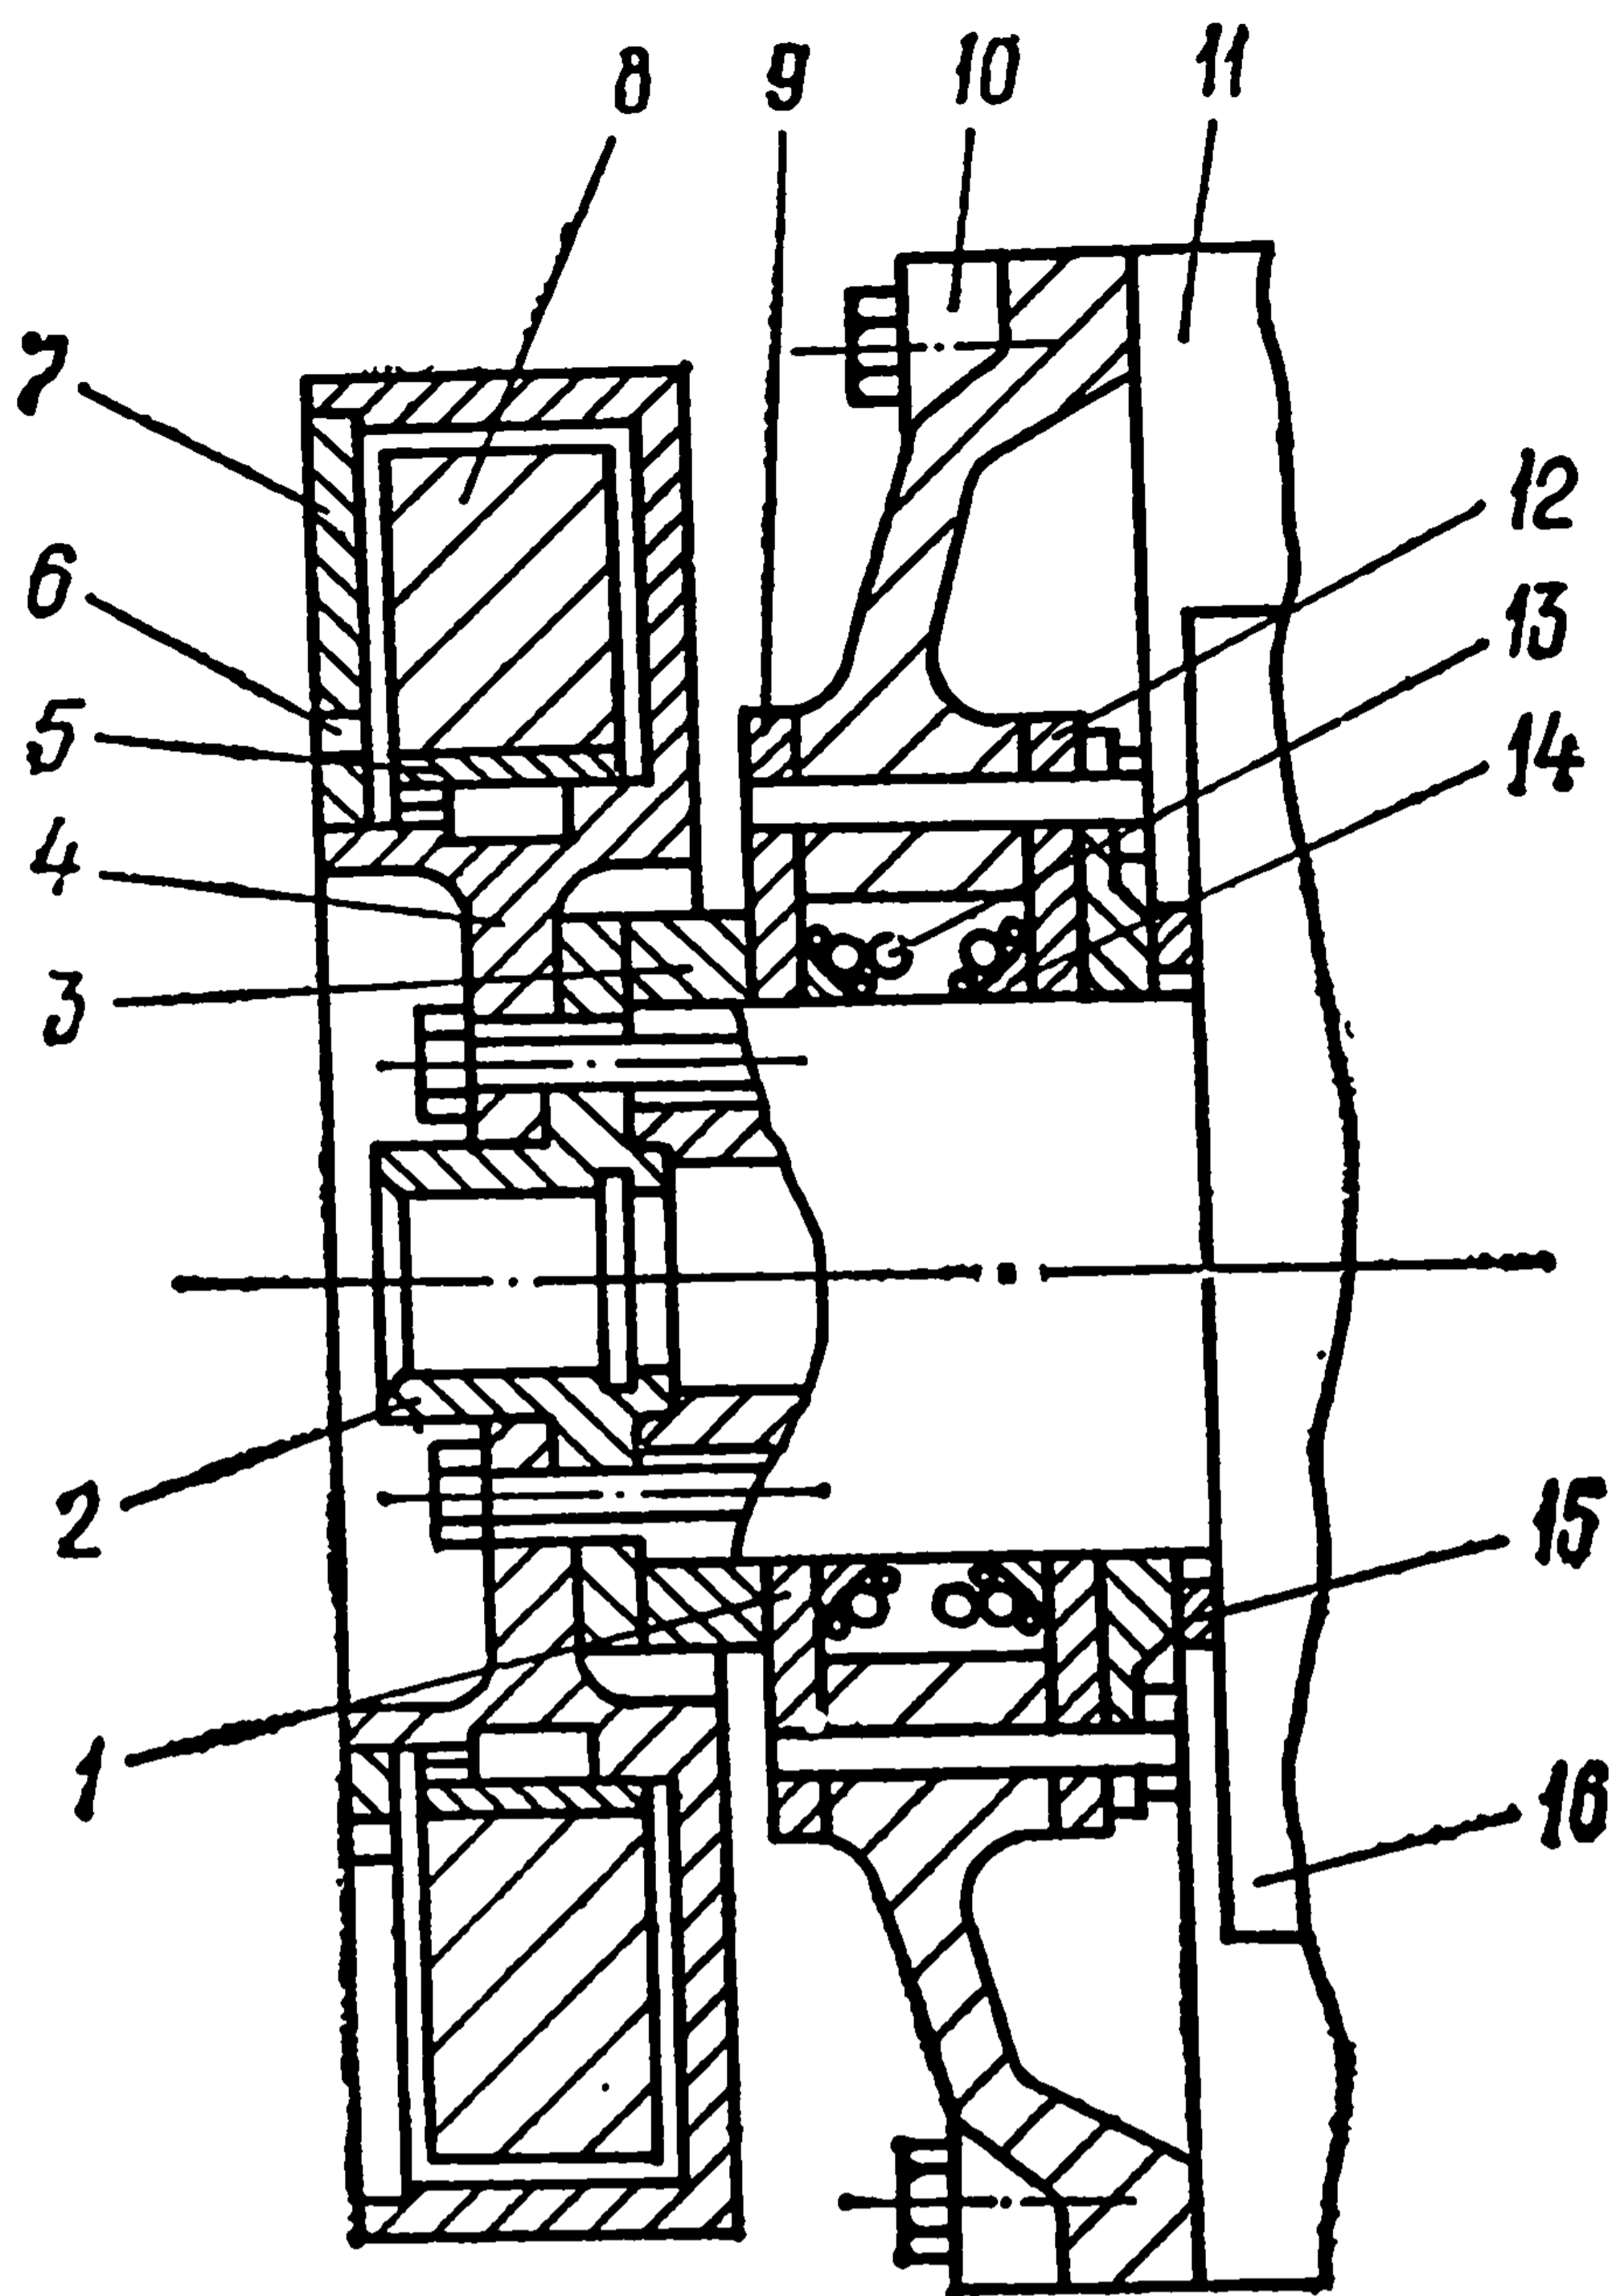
Гаситель крутильных колебаний и упорный подшипник коленчатого вала:
